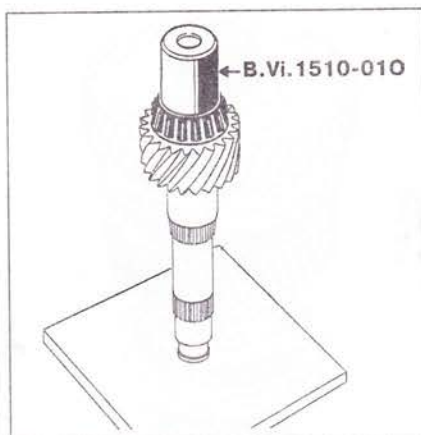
а. Установка подшипников на длинном вторичном вале.
